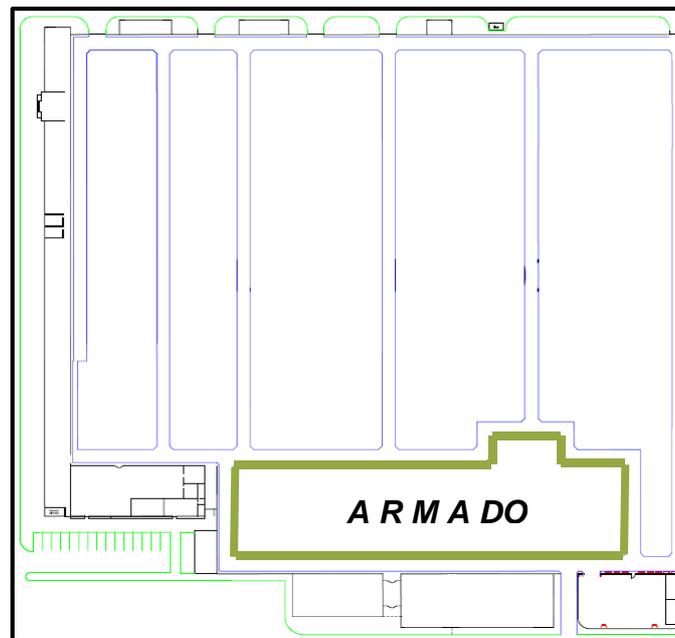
Vista en planta del proceso de armado (Fuente: XYZ SA)
